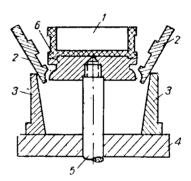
, Разъемная матрица: I- изделие; 2- разъемные боковые части матрицы; 3- обойма; 4- нижняя плита-опора; 5- выталкиватель; 6 — дно матрицы.
